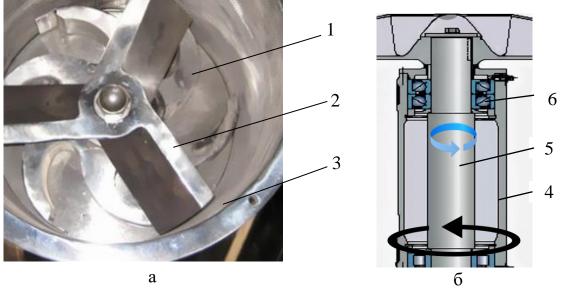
Вид рабочих роторов и схема привода корзинного гранулятора
